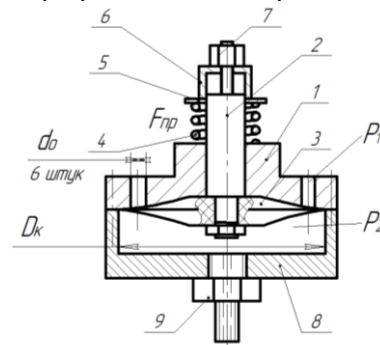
Розрахункова схема зворотного клапану вібраційної машини для очистки забруднень потоком пульсуючого струменя рідини з твердими частинками: 1 – корпус; 2 – шток; 3 – пружина мембрана; 4 – пружина; 5 – шайба; 6 – стакан; 7 – гайка регулювальна; 8 – кришка; 9 – штуцер
